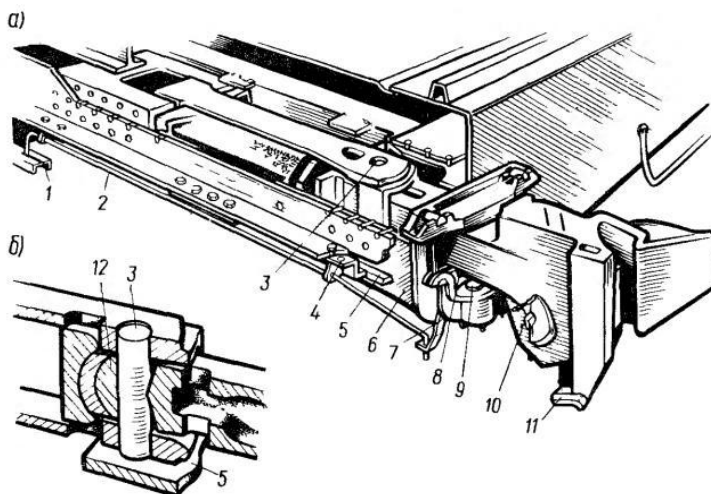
Автосцепное устройство с автосцепкой СА-3М:
